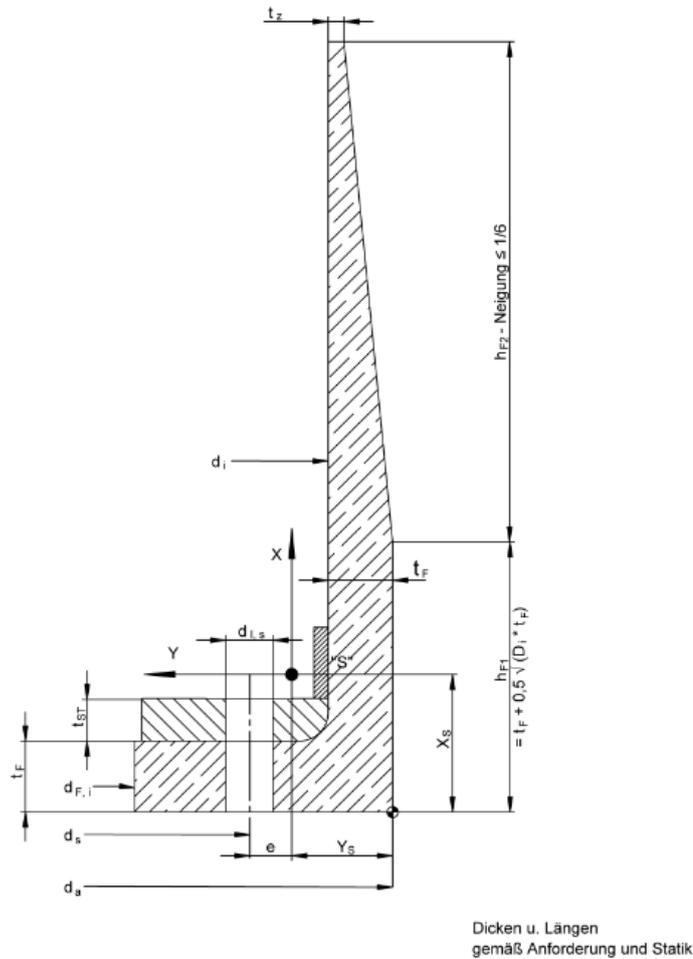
Innenliegender Flansch, Bezeichnungen
